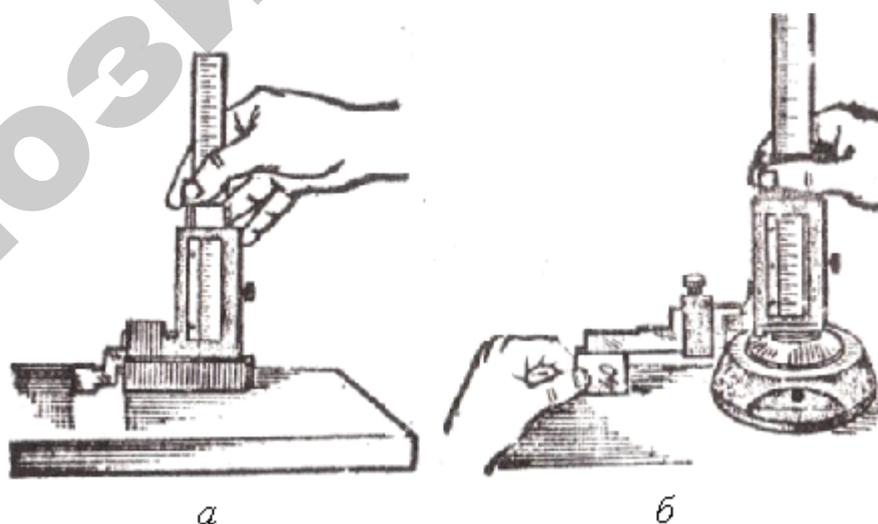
Проверка нулевого положения штангенрейсмусов с пределами измерений:
